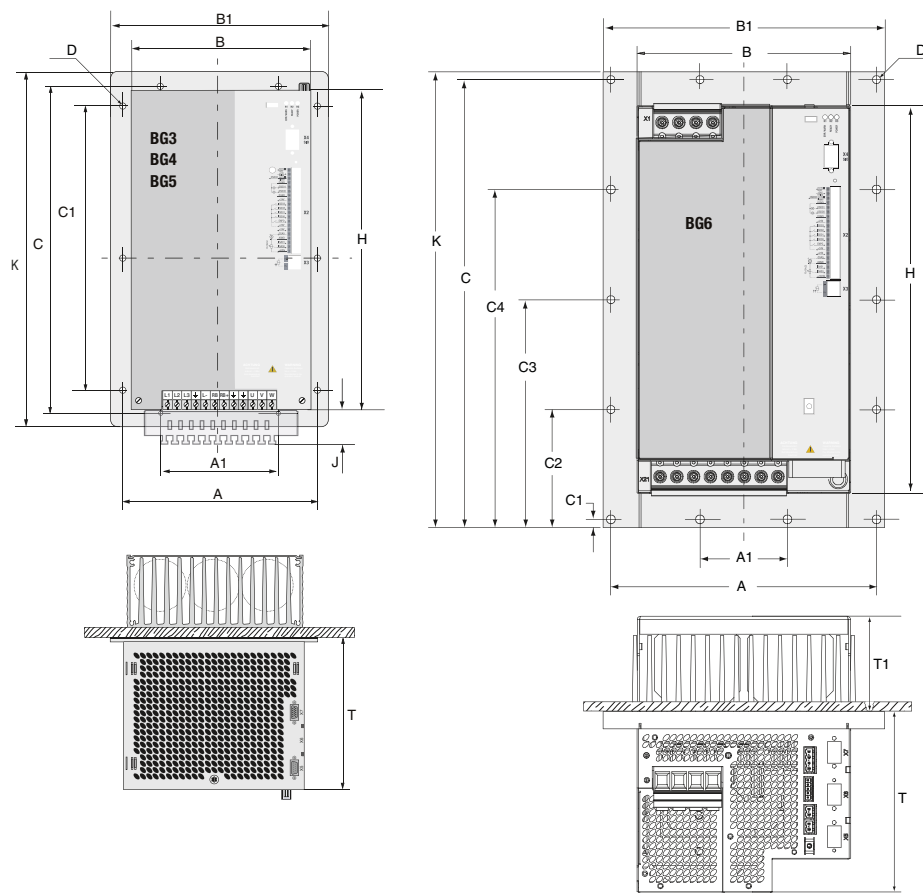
Maßbilder Durchsteckkühlkörper (Maße in mm)
